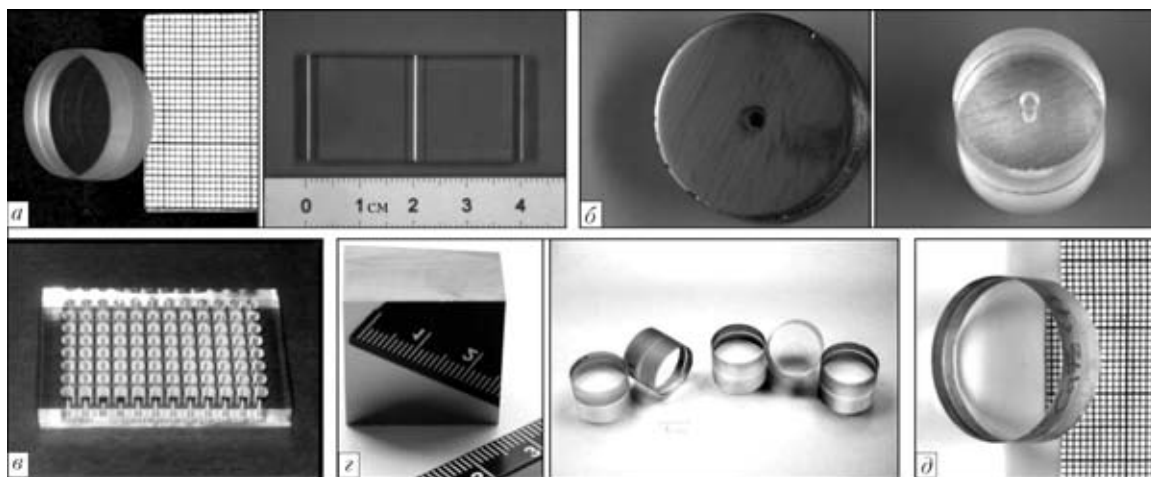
Примеры применения диффузионной сварки в оптике и измерительной технике: а — оптические компоненты; б — стеклокерамика «Ceran» и «Zerodur» для деталей измерительной техники; в — титровые пластины из боросиликатного стекла; г — оптические детали из инфракрасных стекол и марки BK7 для аэрокосмической техники; д — кристаллы (фторид кальция и магния, сапфир, Nd:YAG) для микролитографии и лазерной техники
